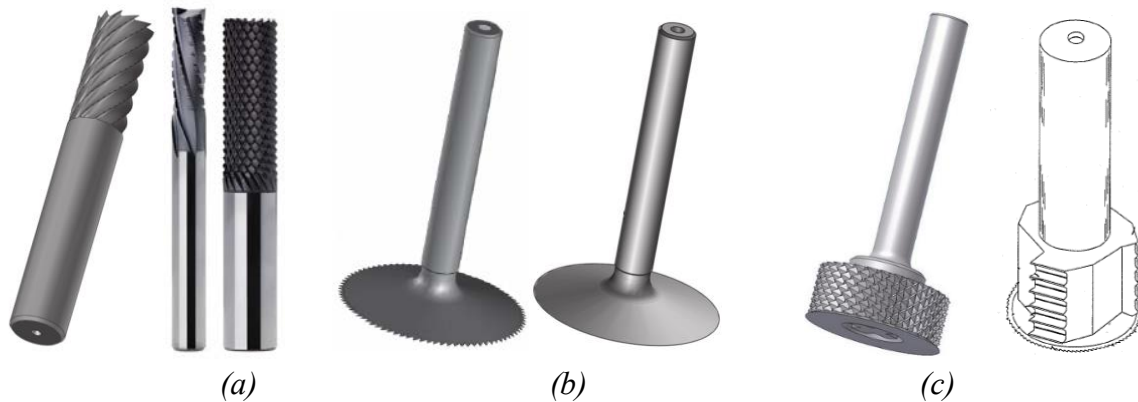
Famille d'outils utilisés pour l'usinage de nid d'abeilles : (a) outil monobloc, [120,122] ; (b) outil soupape, [120] ; (c) outil combiné, [120,121].
